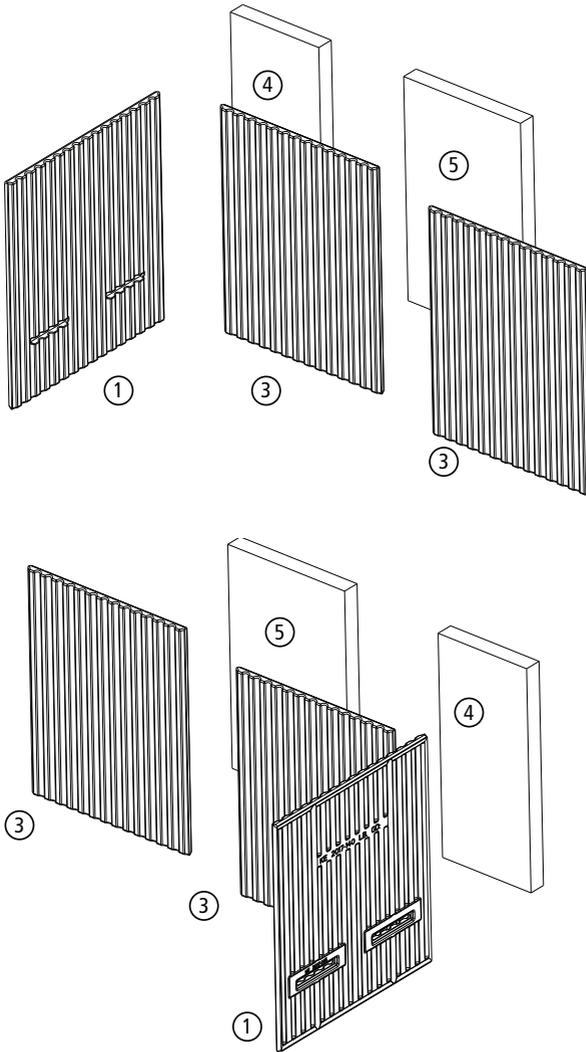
Revêtement de la chambre de combustion FINA ES
